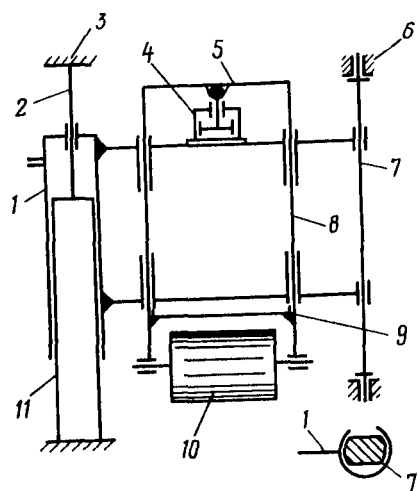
Кинематическая схема верхних ворот лесопильной рамы 2Р75-1: 1 — корпус, 2 — направляющая, 3, 6 — кронштейны, 4, 11 — гидроцилиндры, 5 — коромысло, 7, 8 — штанги, 9 — траверса, 10 — валец
